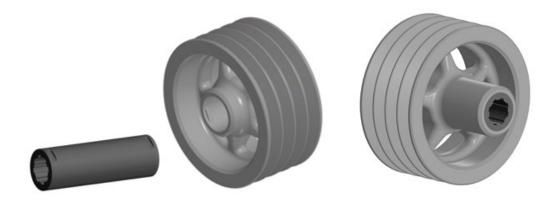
Втулка, колесо из оргстекла и готовый шкив (слева направо)
